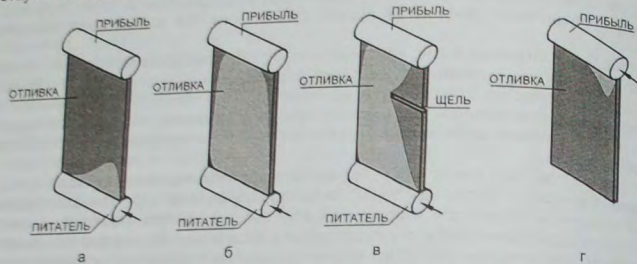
Расположение питтинговой коррозии на поверхностях отливок из стали 08X14H7МЛ
